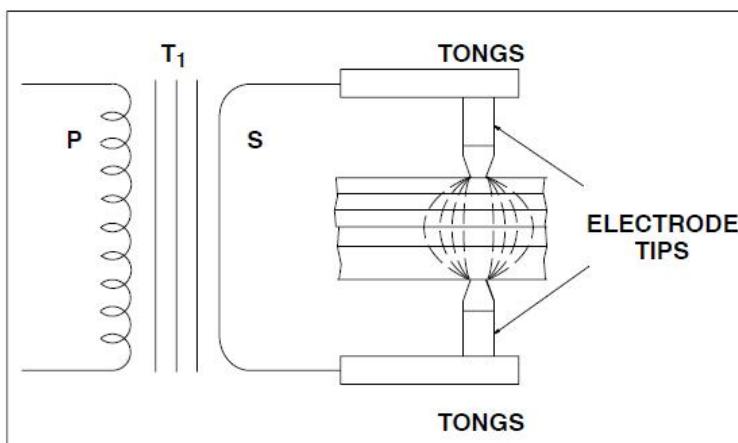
Widerstandspunktschweiß-Wärmezonen
